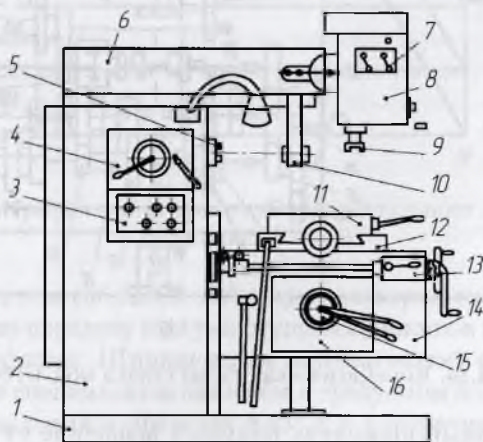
Общий вид станка мод. 6Т80Ш:
